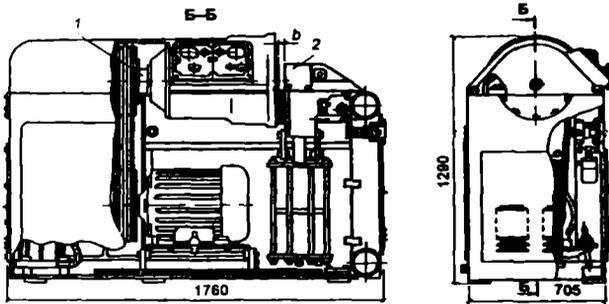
Машина МСТ-35 для стыковой сварки трением:
